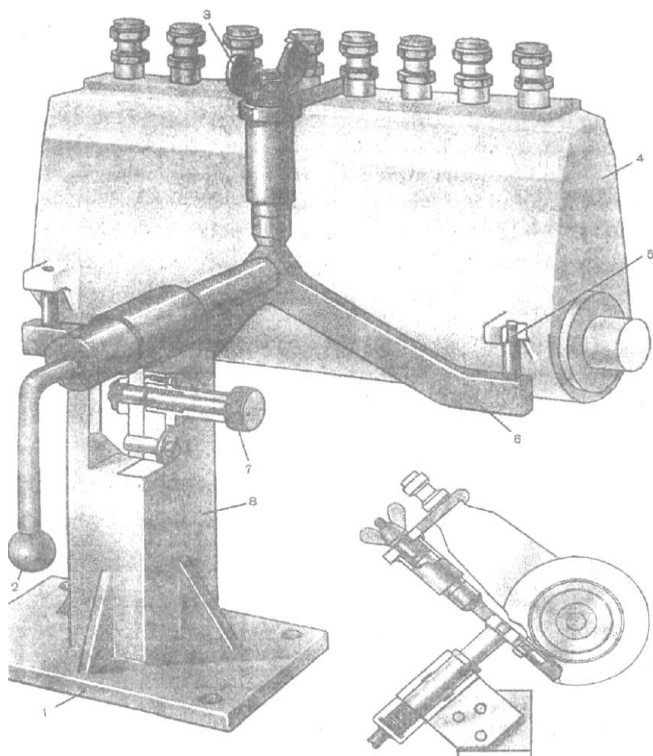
Загальний вигляд пристрою для розбирання насосів ЯЗТА: 1 – плита; 2 – рукоятка; 3 – гайка баранчата; 4 – паливний насос 238НБ; 5 – штифт-фіксатор; 6 – кронштейн; 7 – фіксуючий гвинт; 8 – стійка.
